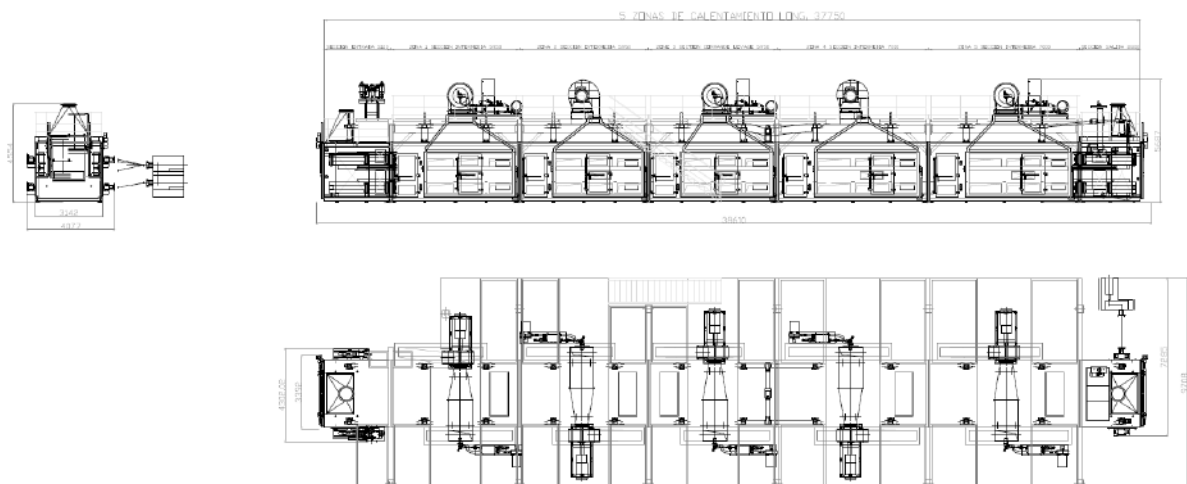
Vistas del horno de polimerización en alzado, planta y perfil.
